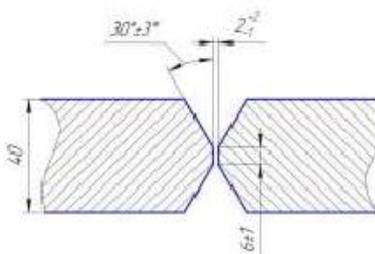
Конструктивные элементы подготовленных кромок сварного соединения
